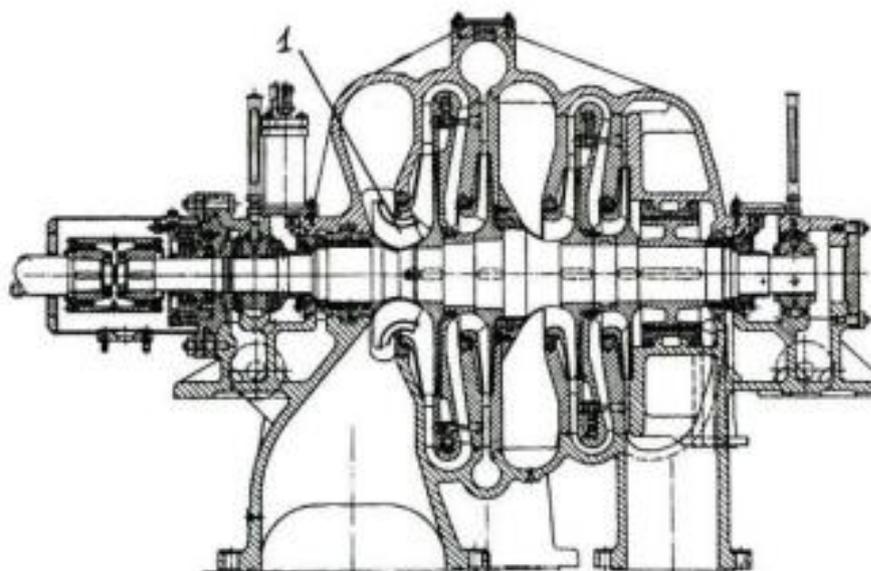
Холодильный центробежный компрессор: 1 - входной направляющий аппарат
